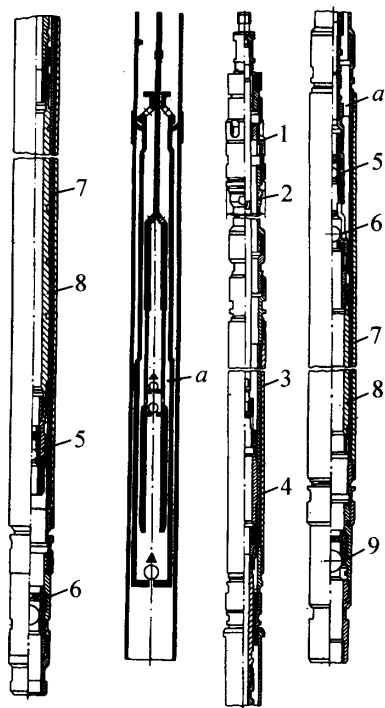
Глубинные штанговые насосы: а) – НСВГ-38/55; б) – НСВГ-55/43; в) – НСВД; 1 – противопесочный клапан; 2 – замок; 3 – верхний цилиндр; 4 – верхний плунжер; 5 – нагнетательный клапан; 6 и 9 – всасывающие клапаны; 7 – нижний цилиндр; 8 – нижний плунжер
